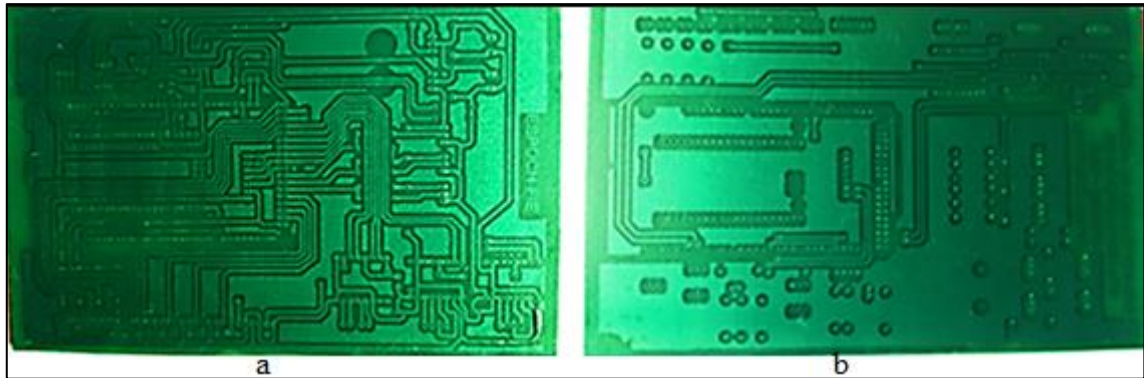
Placa con mascarilla de soldadura en las pistas a) Vista inferior b) Vista superior
